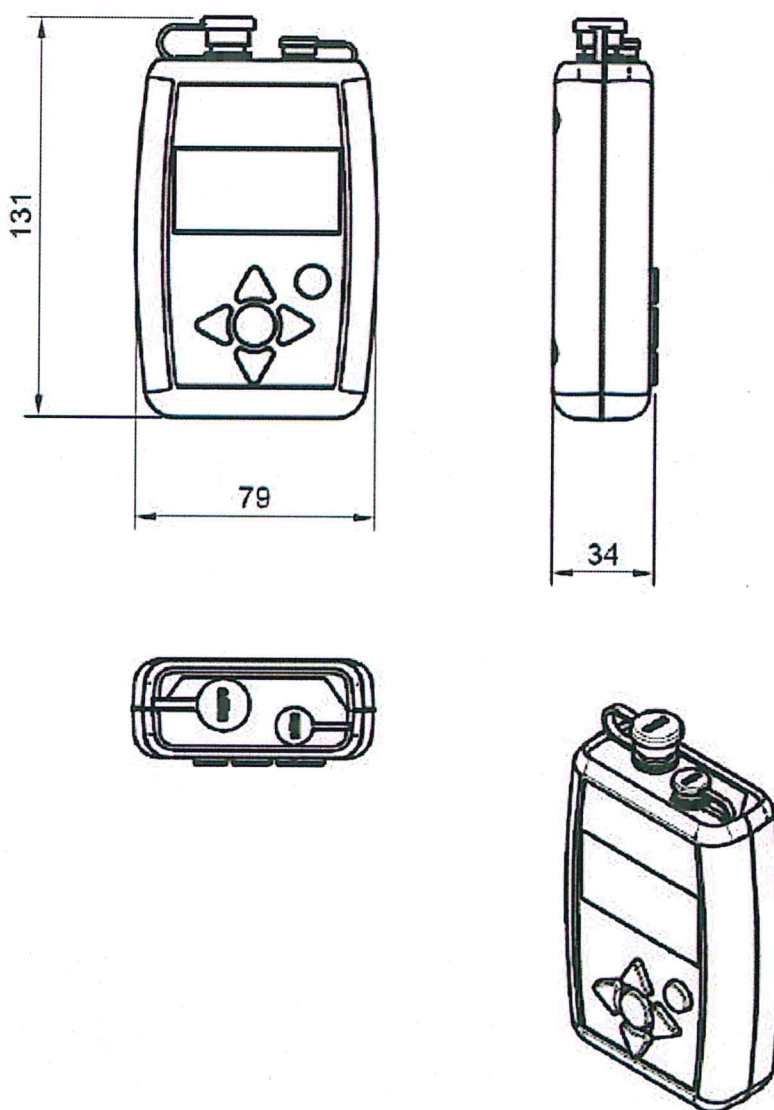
Габаритные размеры СТ и конструктивное исполнение.
